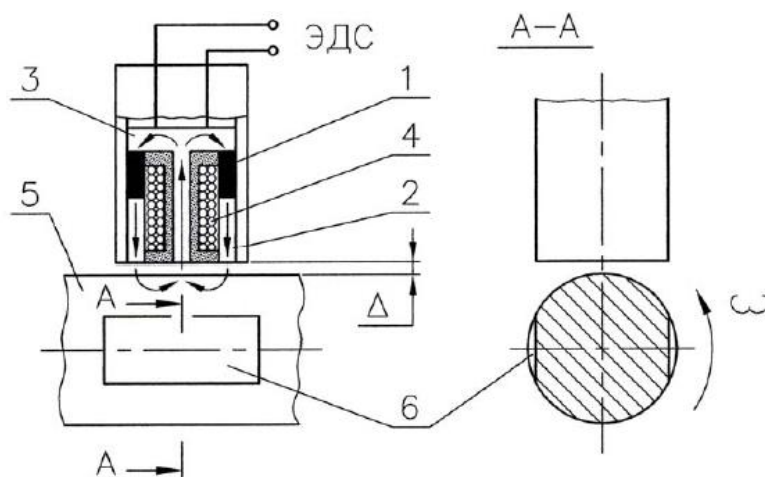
Конструктивна схема індукційного датчика і пристрою для вимірювання числа обертів валу
